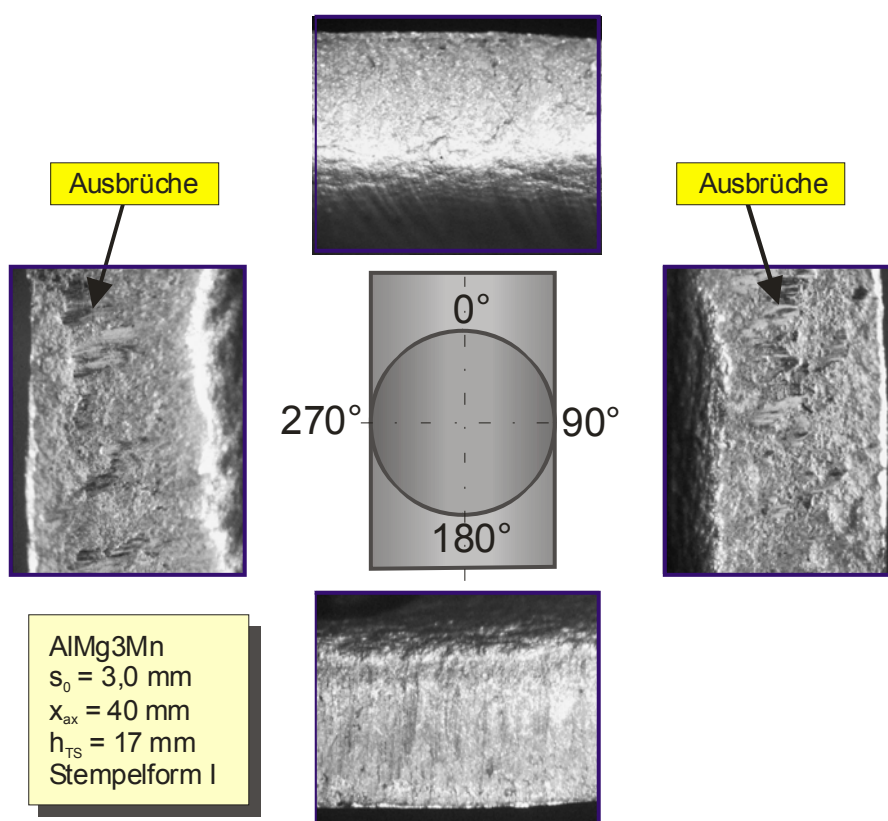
Schnittflächenausbildung beim IH-TAS (AlMg3Mn; 3,0 mm)
